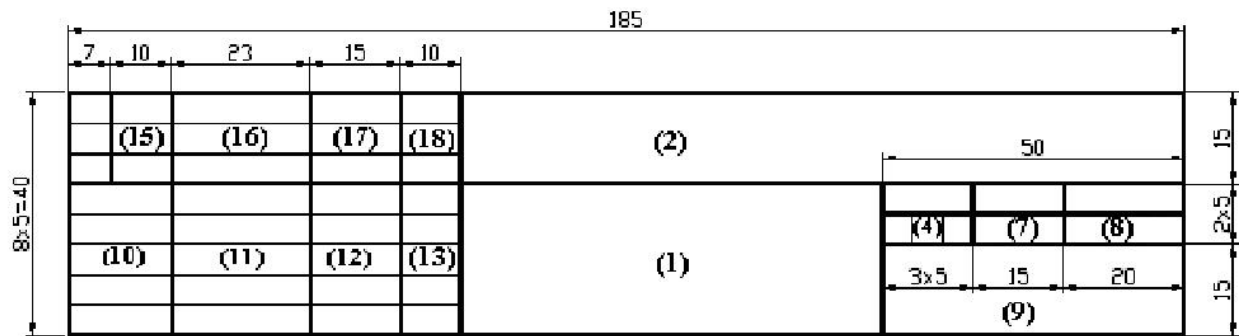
Размеры основной надписи для текстовых конструкторских документов (первый или заглавный лист)
